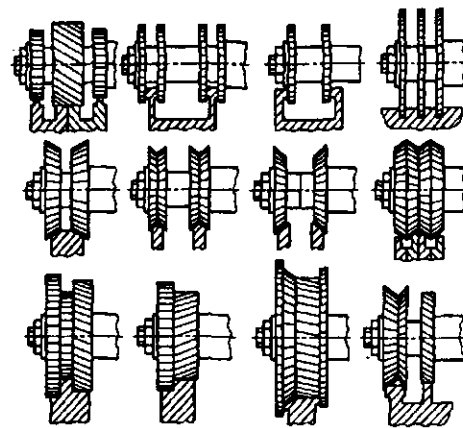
Фрезы, используемые для обработки плоскостей корпусных деталей
